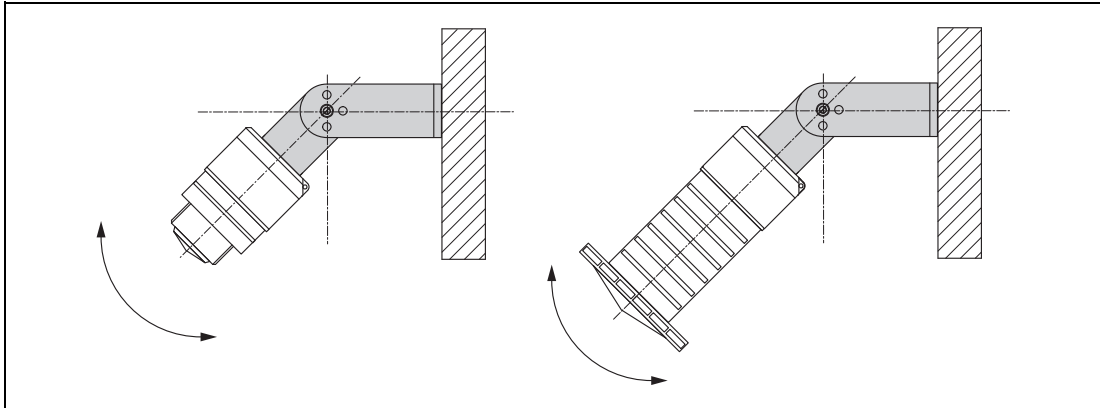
Einbau mit Montagebügel ausrichtbar
